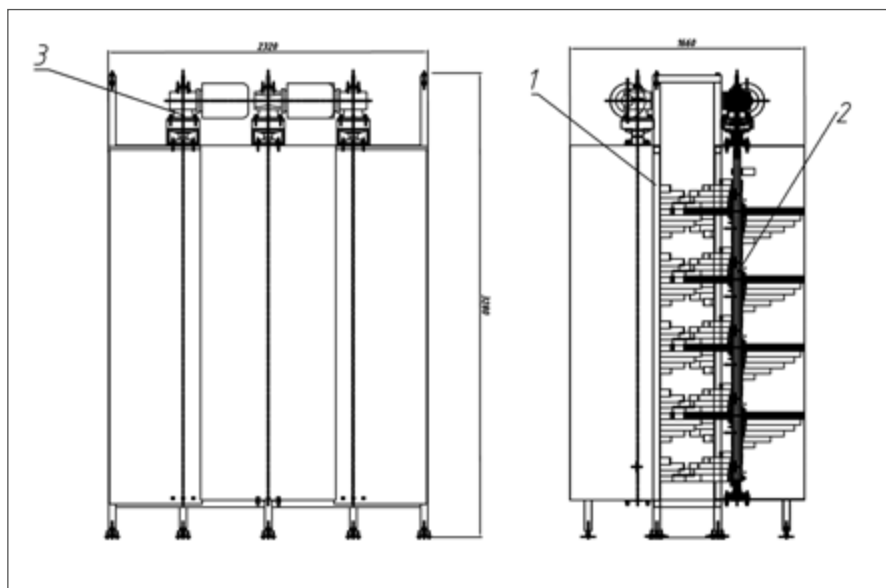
Общий вид моечной машины: 1 – сварной каркас; 2 – моечные валы; 3 – мотор-редукторы
